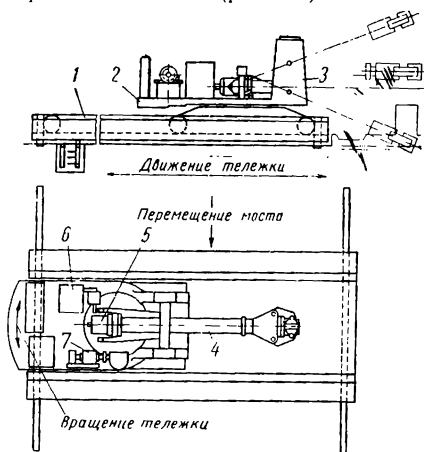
Схема мостового ширококолейного манипулятора с поворотной тележкой (II типа): 1 — мост; 2 — тележка; 3 — механизм подъема хобота; 4 — хобот; 5 — механизм поворота хобота; 6 — механизм подъема хобота; 7 — механизм поворота тележки
